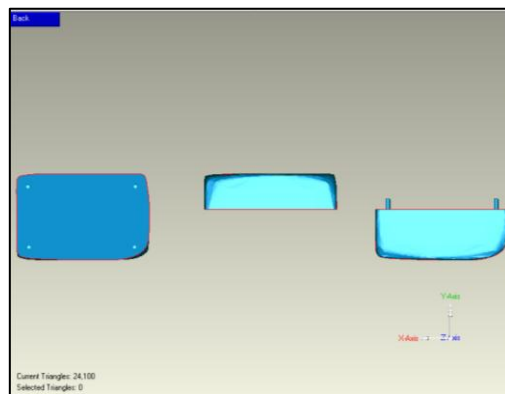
Colocar guías en el molde para un mejor ensamble.
